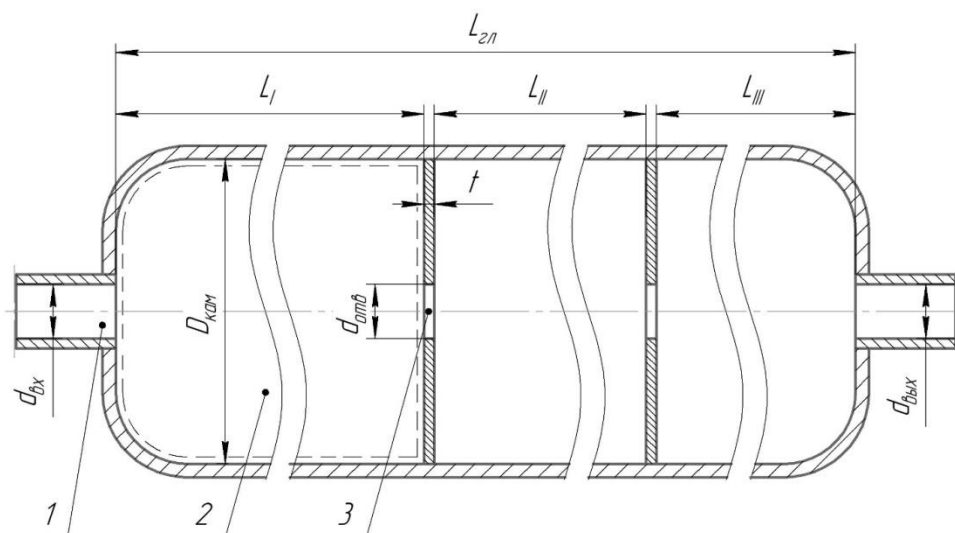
Конструктивная схема трёхкамерного глушителя
